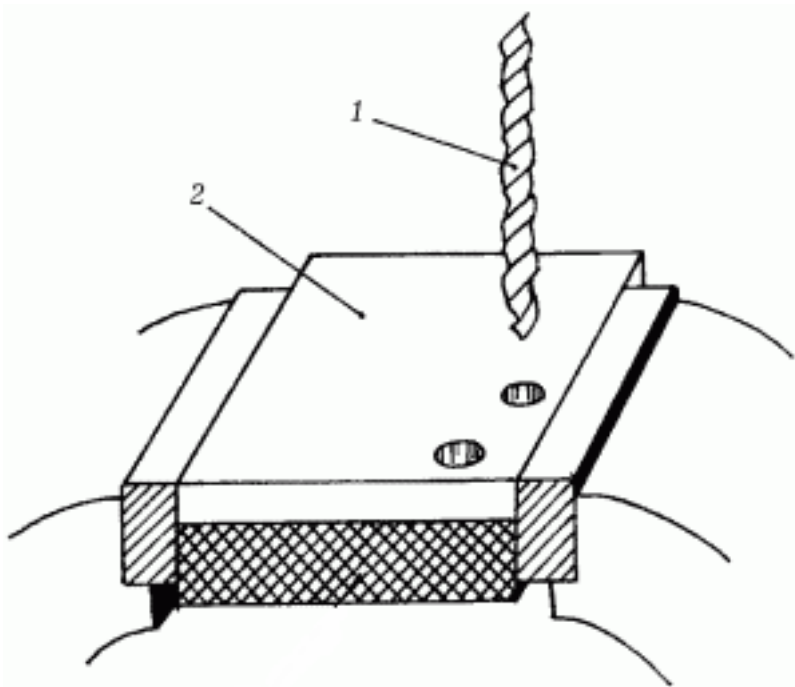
Схема сверления где 1 – сверло; 2 —деталь
